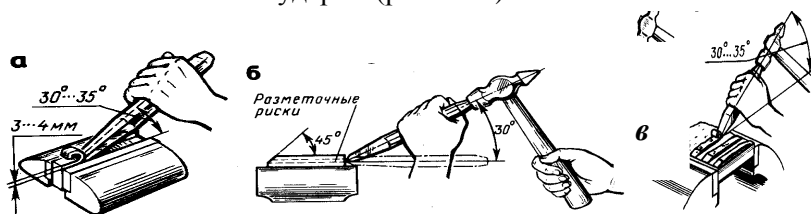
Рубка полосового (а), листового (б) металла и широких поверхностей (в)
